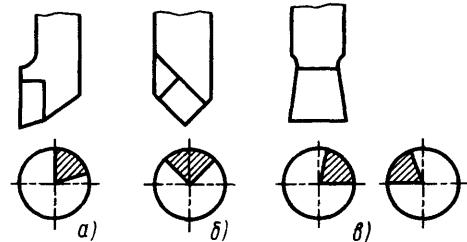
Схемы (а—в) привязки в визире микроскопа режущих кромок резцов
